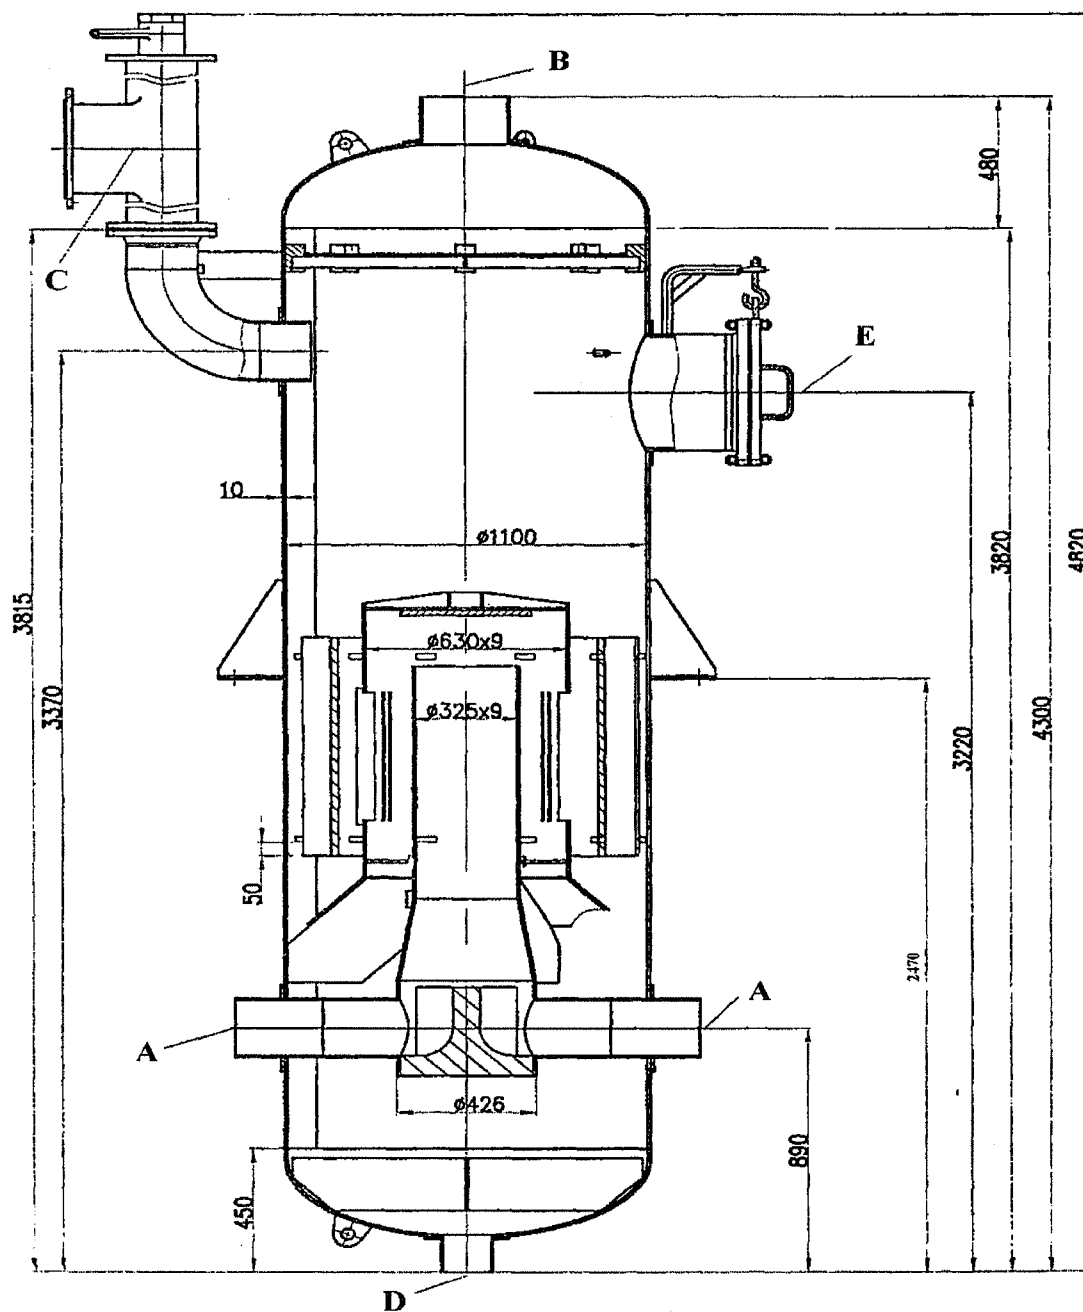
Габаритный чертеж расширителя продувки парогенераторов
